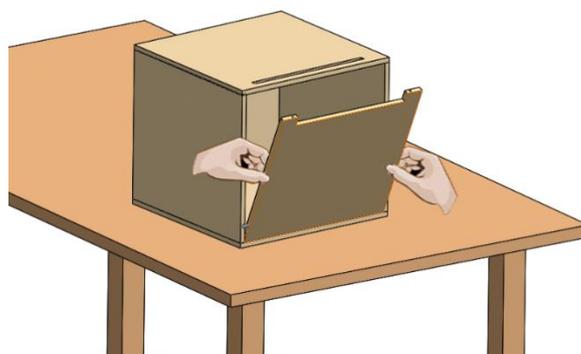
Paso 16 del ensamblaje del cajón (conjunto 2)
